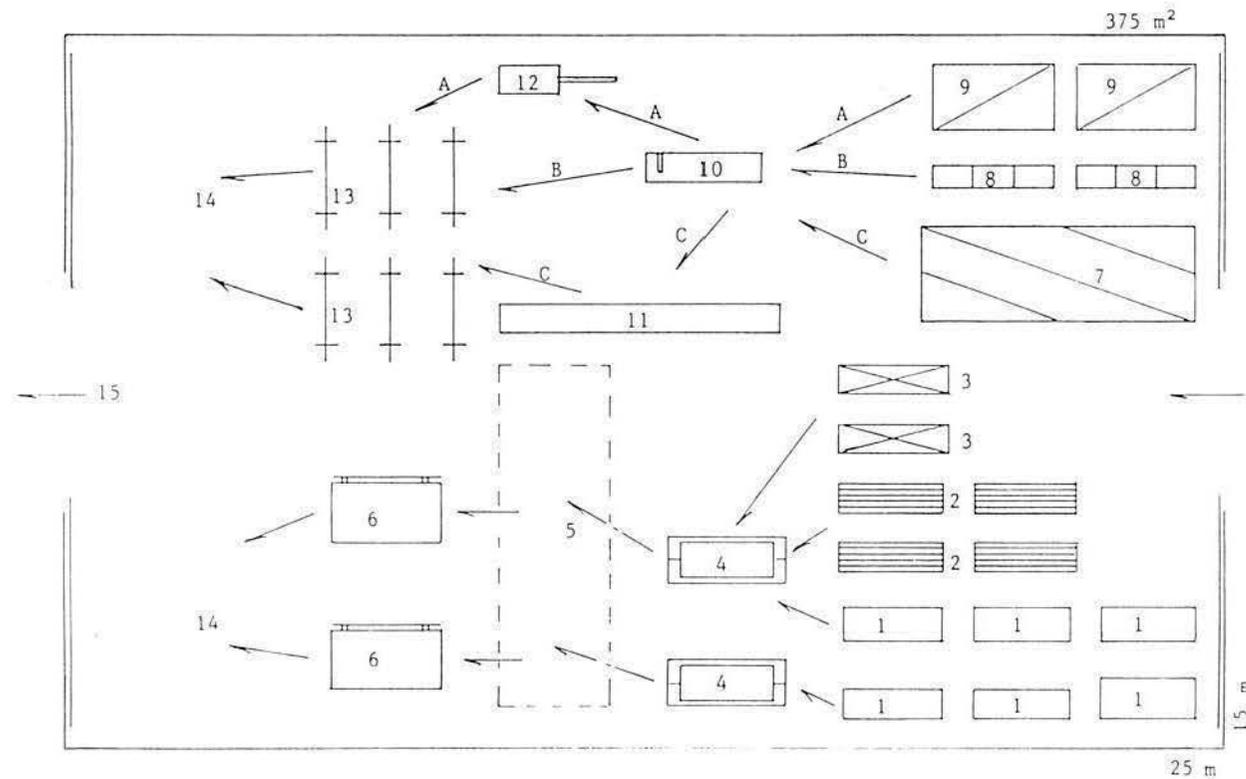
Exemplo de Desenvolvimento de Layout:
